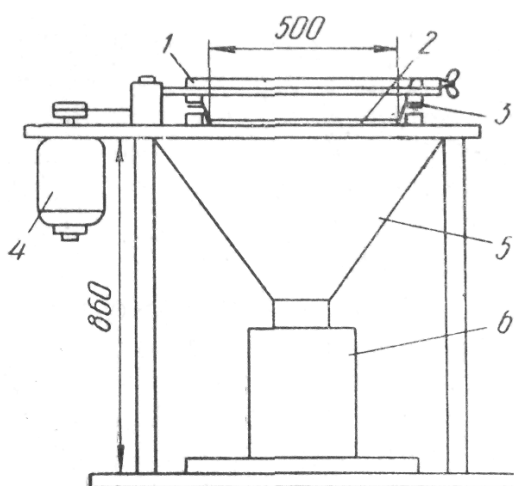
Схема вібраційного сита: 1 - обичайка; 2 - полотно(сітка) сита; 3 - пружини; 4 - електродвигун; 5 - вирва; 6 - прийомний бачок.
